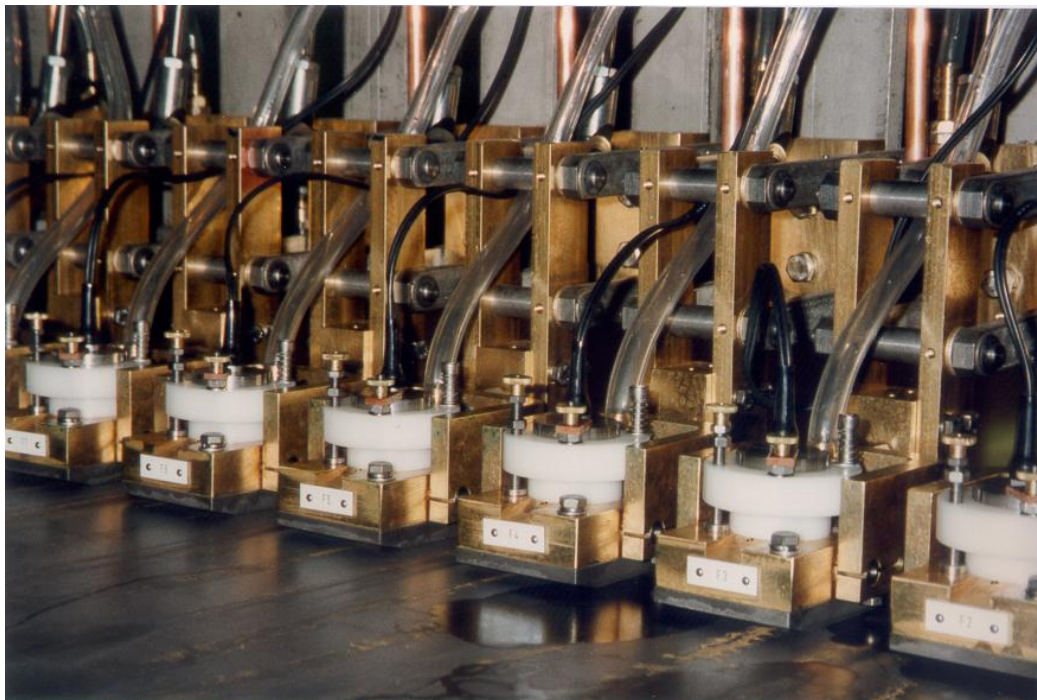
Gehärtete Gleitsohlen führen die kardanisch aufgehängten Prüfköpfe auf der Band-Oberfläche.
